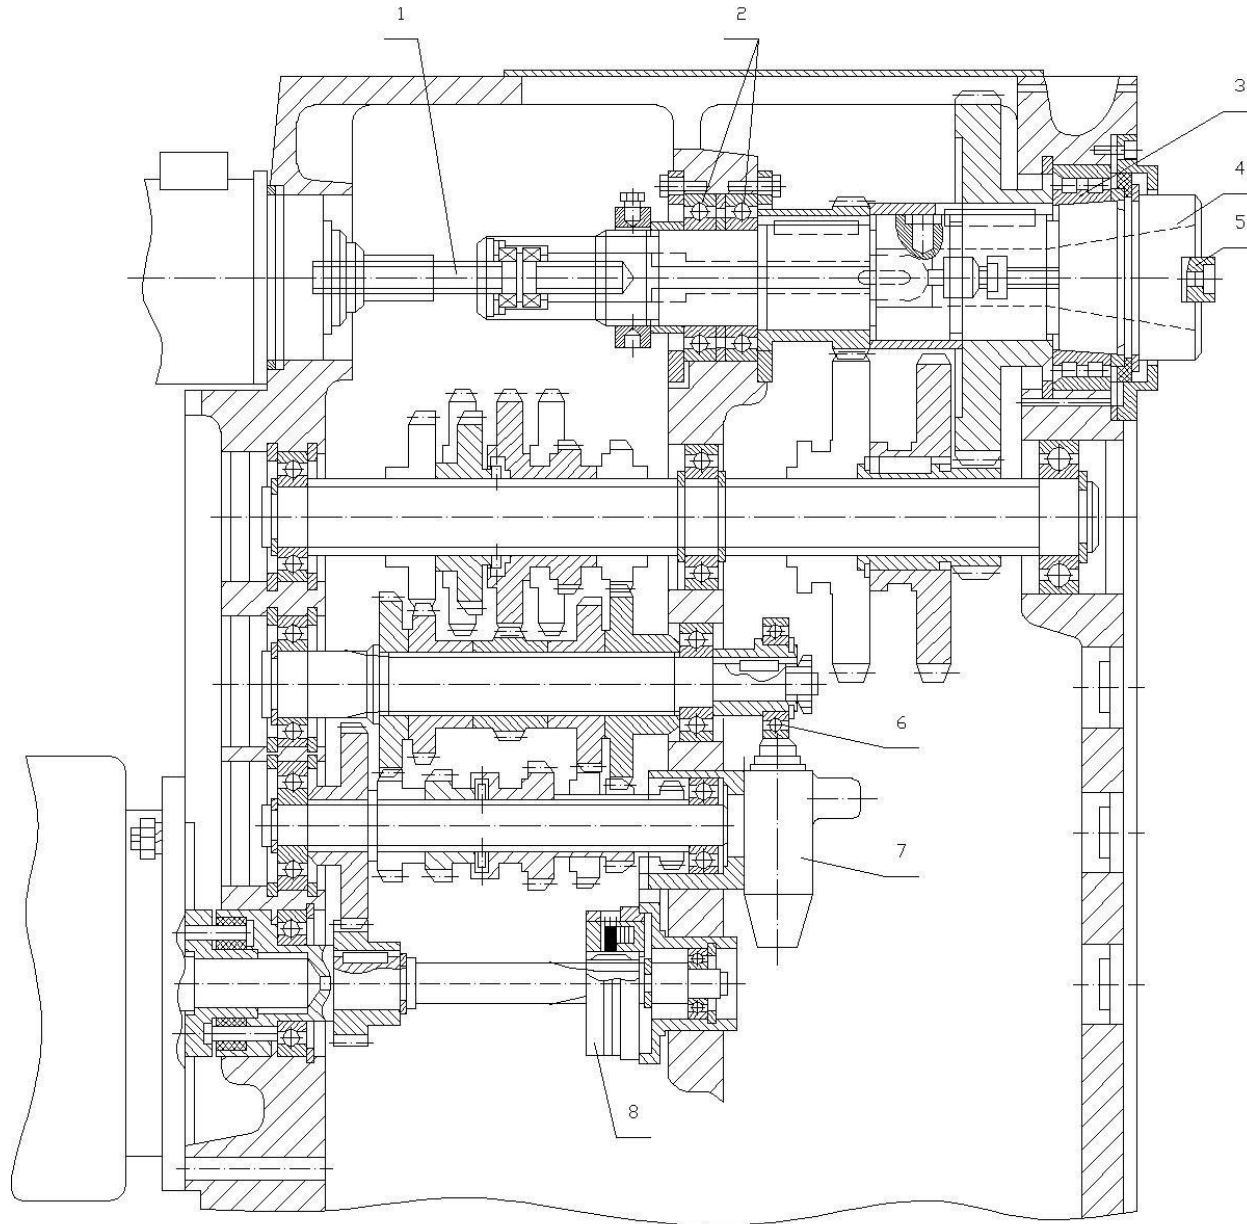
Привод главного движения горизонтально-фрезерного станка.
